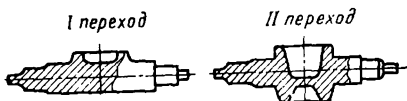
Двухпереходная штамповка в разъемных матрицах
